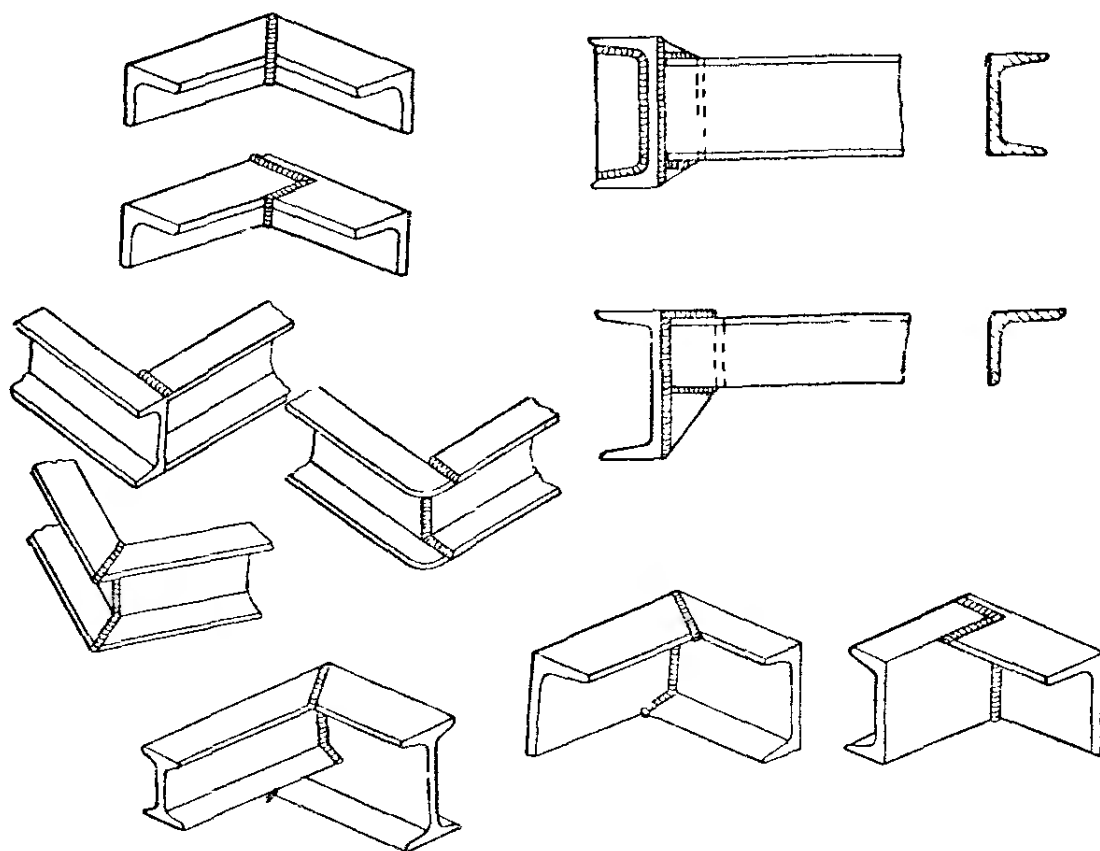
Примеры сварки узлов из профильного проката
